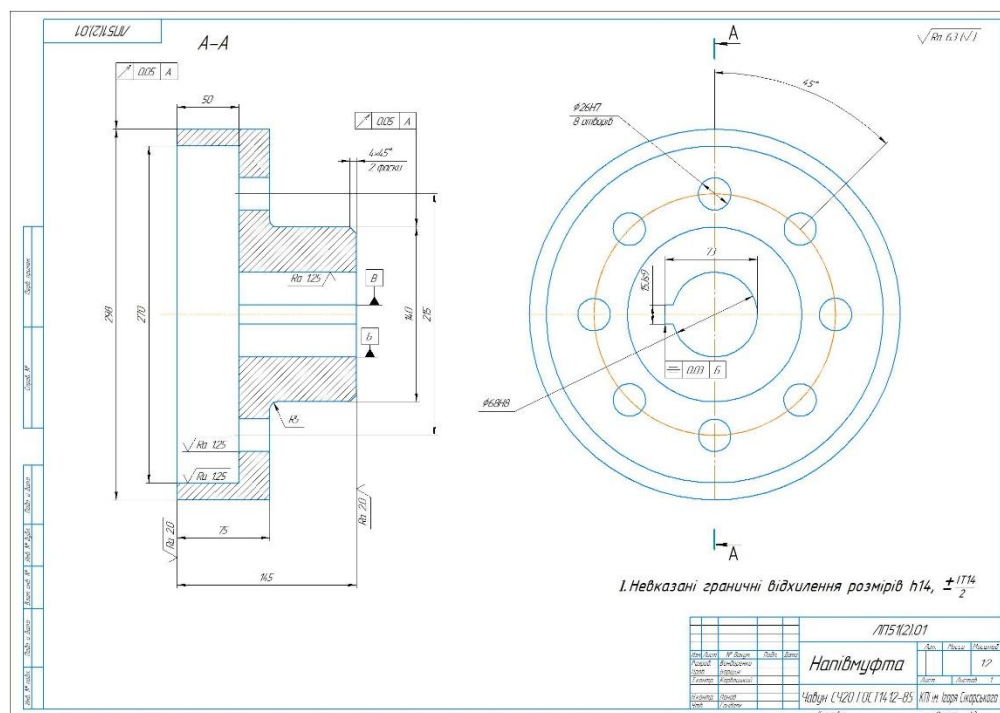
Ескіз деталі "Напівмуфта"
